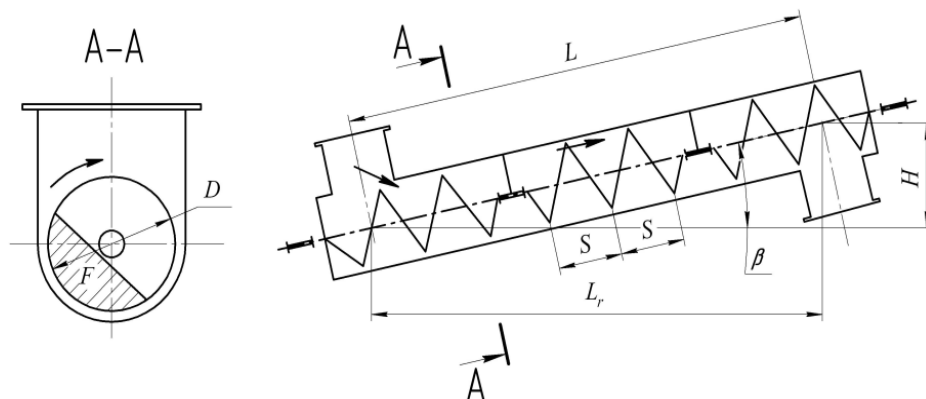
Розрахункова схема гвинтового транспортера зерноочисної машини
